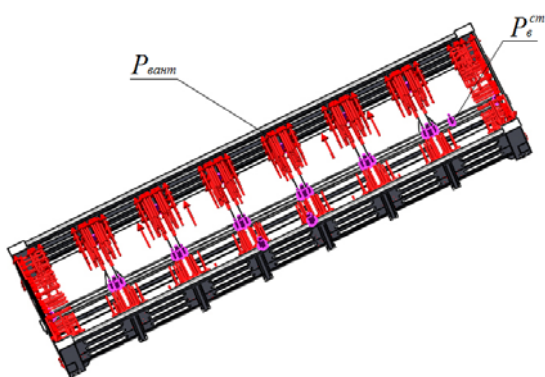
Розрахункова схема несучої конструкції напіввагона при розвантаженні грейферним ковшем (вид зверху)
